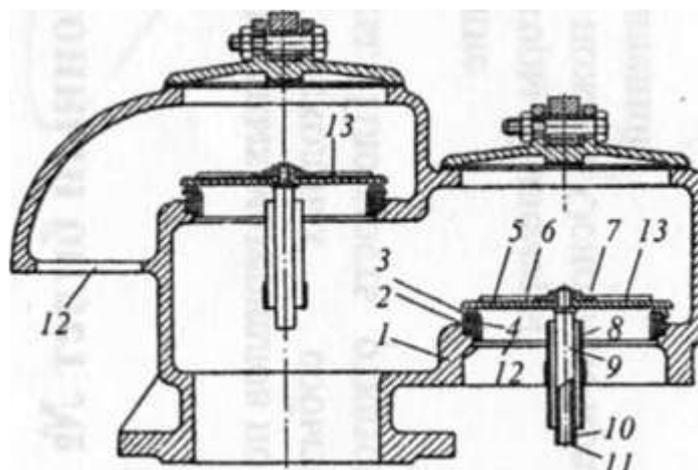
Немерзающий дыхательный клапан типа ДК: 1 - корпус; 2 - кольцо; 3 - седло; 4, 6 и 10 - фторопластовые покрытия; 5 - тарелка; 7 - гайка; 8 - направляющая фторопластовая втулка; 9 - шток; 11 - стержень; 12 - сетка; 13 - грузы
